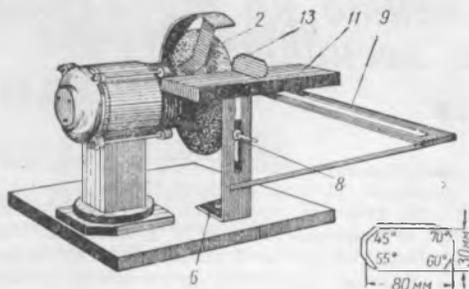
Установка (по шаблону) угла заточки режущей грани зуба пилы: 2 — точильный круг; 6 — нижняя часть передвижного столика; 8 — закрепительный болт вертикальной стойки столика; 9 — передвижной треугольник столика; 11 — доска столика; 13 — установочный шаблон.
